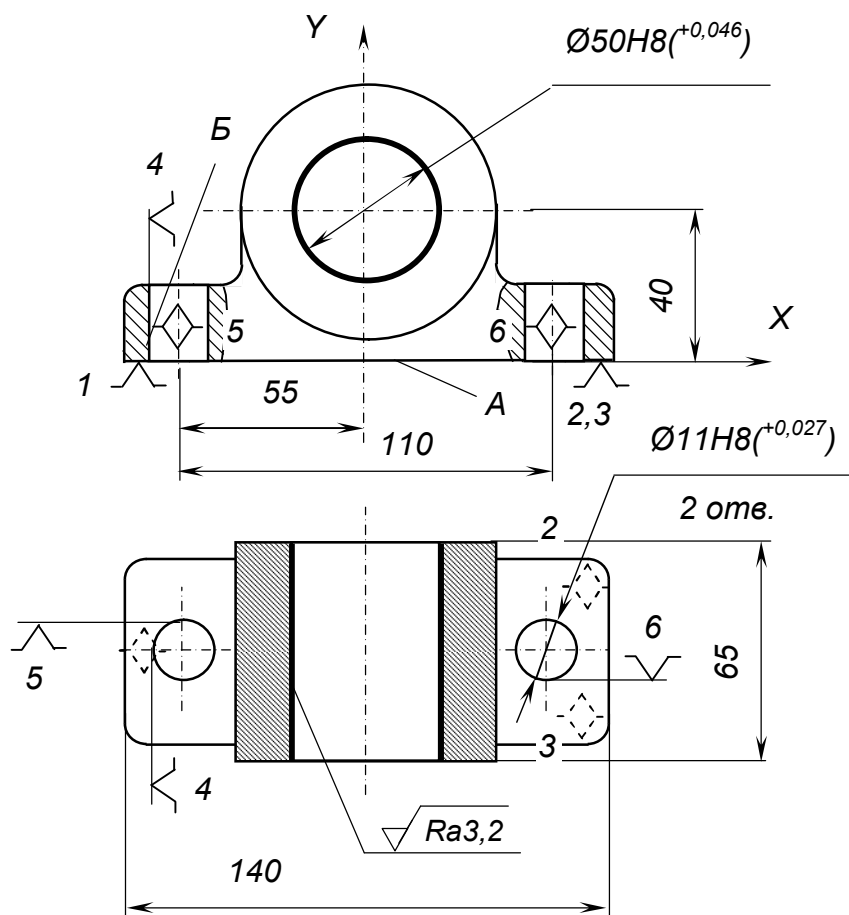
Ескіз зі схемою базування на операції обробки отвору в деталі типу «корпус підшипника»
